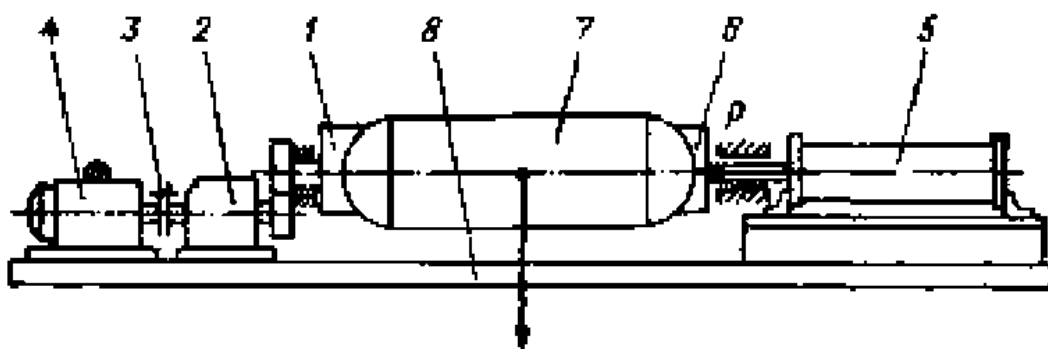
Двухстоечный кантователь с торцевыми планшайбами
